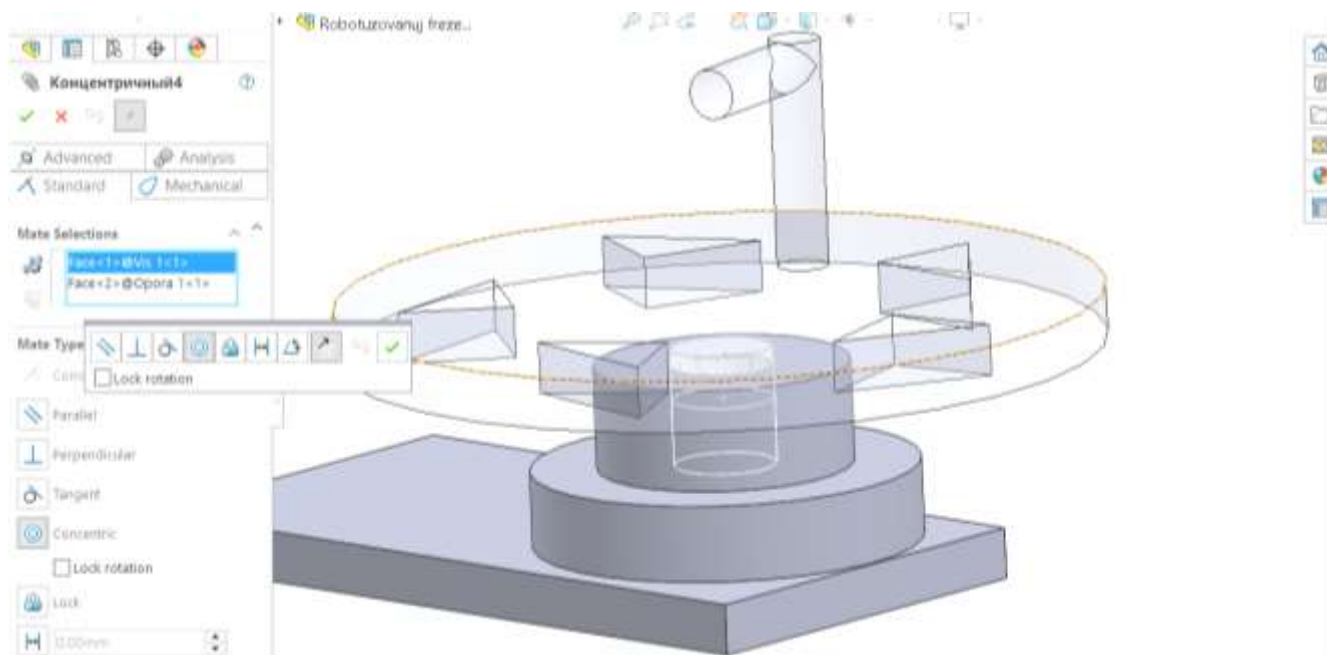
Розташування фрикційного колеса повороту в опорі.
